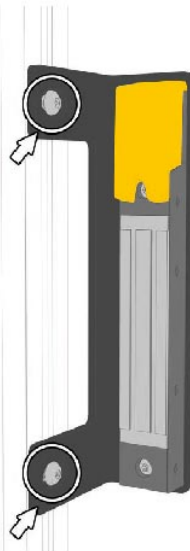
Montageplatte mit Prozesszuhaltung am Profil anbringen und und Schrauben M8 x 12 mm Torx festziehen.
